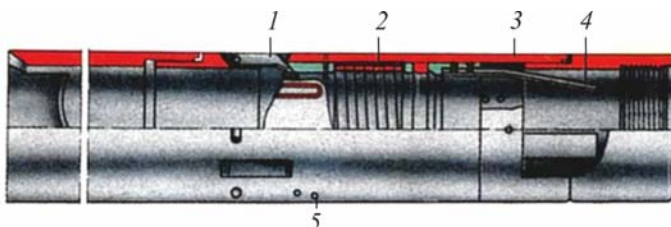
Наружная труборезка: 1 – резец; 2 – спиральная пружина; 3 – корпус; 4 – плоская пружина; 5 – штифты
